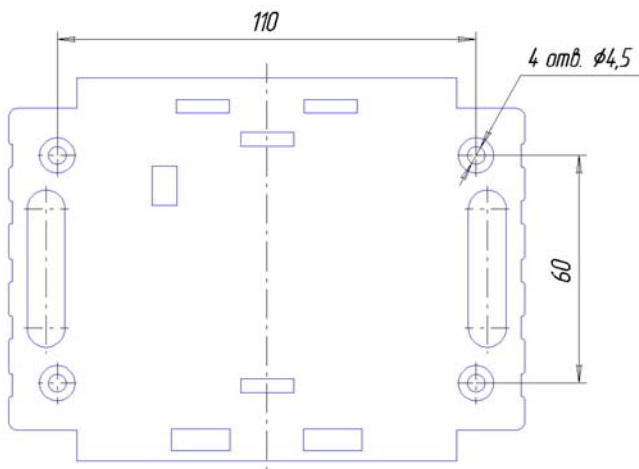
Крепление адресного блока (присоединительные размеры)
